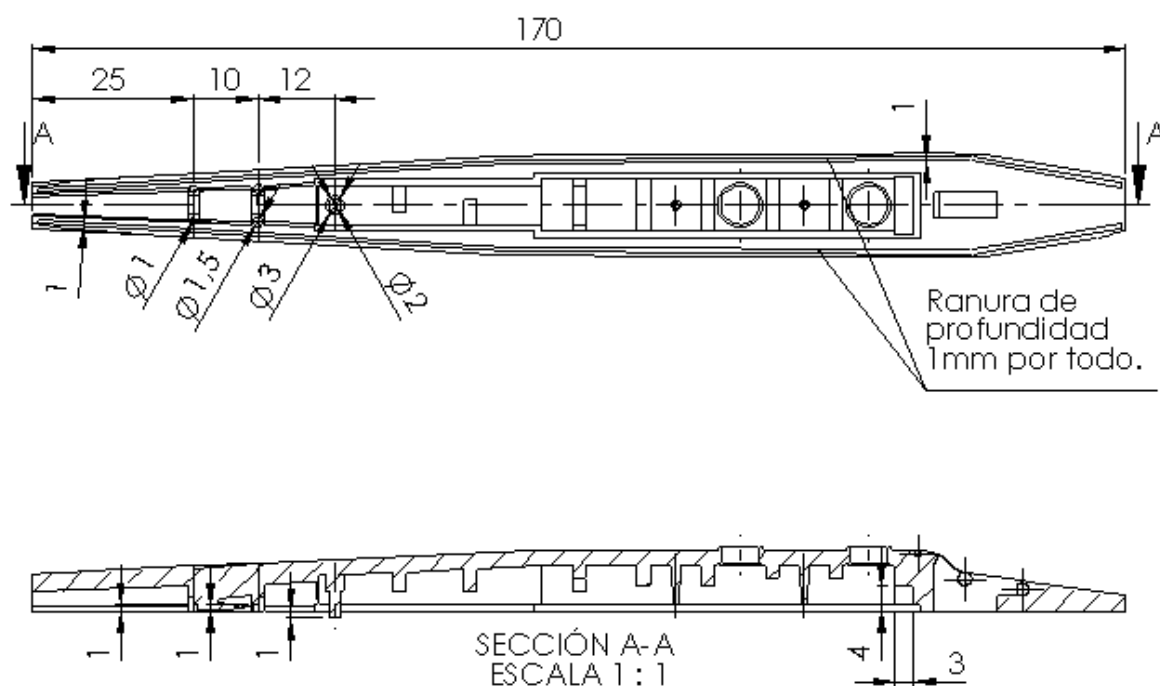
Carcassa superior. Vista de de planta (figura superior) i secció A-A de la vista de planta (figura inferior).
